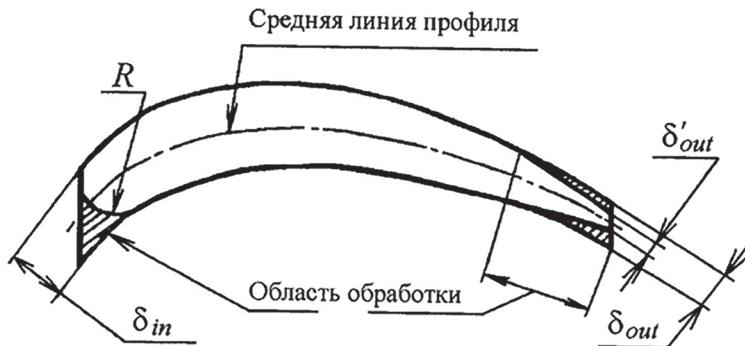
Типовая схема слесарной обработки кромок рабочих колес гидротрансформатора
